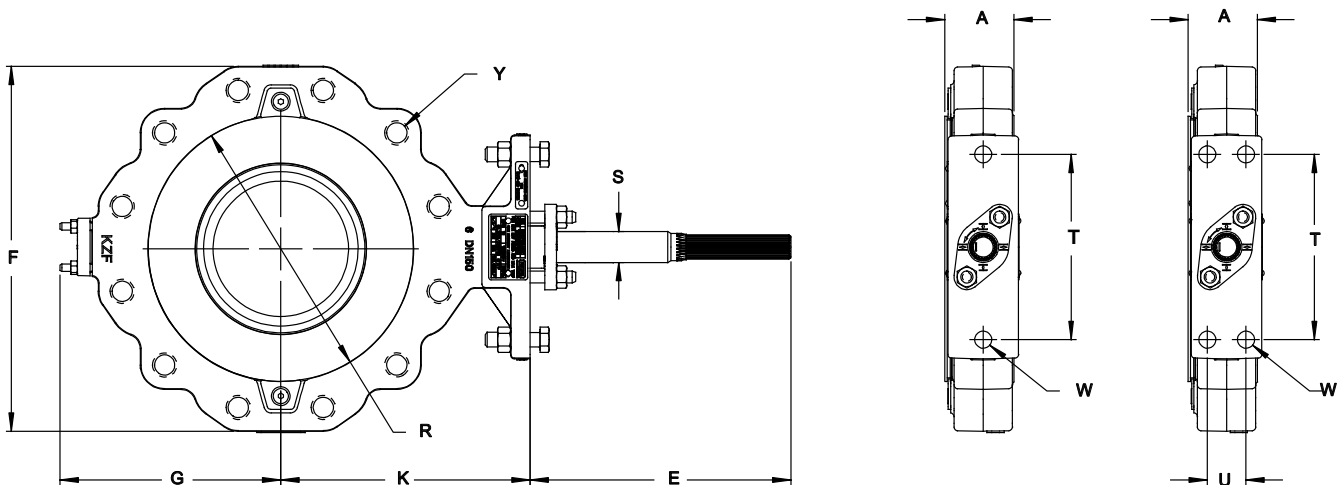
Размеры затвора Control-Disk в корпусе с проушинами
